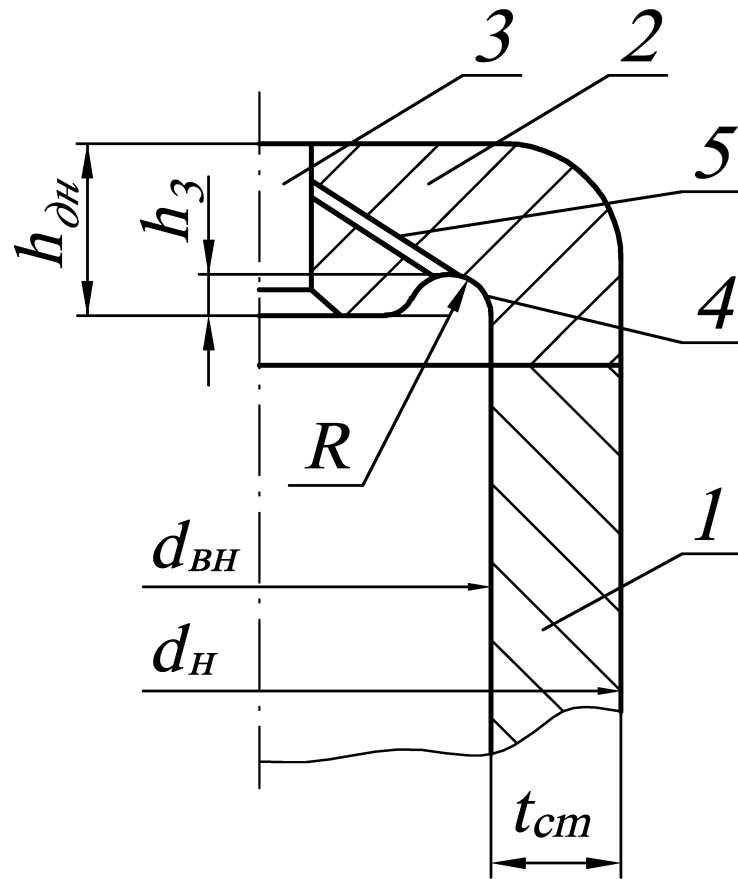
Корпус рабочего цилиндра [333]
